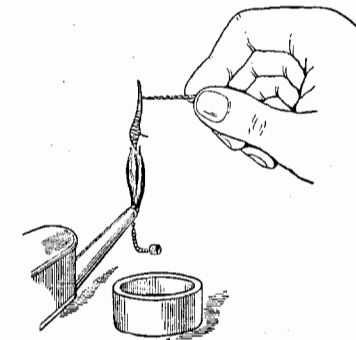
Закалка для крепления пружины во время чистовой обработки (показано стрелкой).
